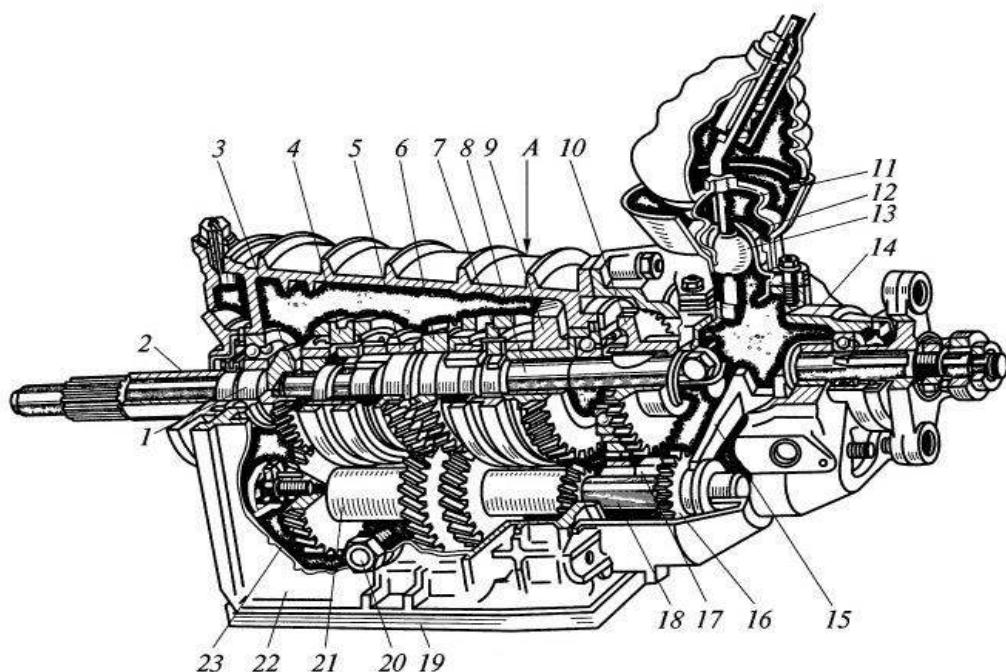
Конструкция трёхвальной коробки передач автомобиля ВАЗ:
